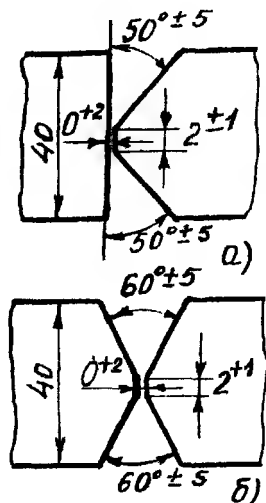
Виды разделок кромок под сварку
